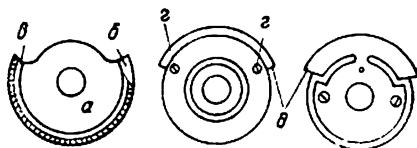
Фреза зубоотделочной машины: *а* — фреза; *б* — входная часть; *в* — выходная часть; *г* — регулировочные винты; *д* — поводок
